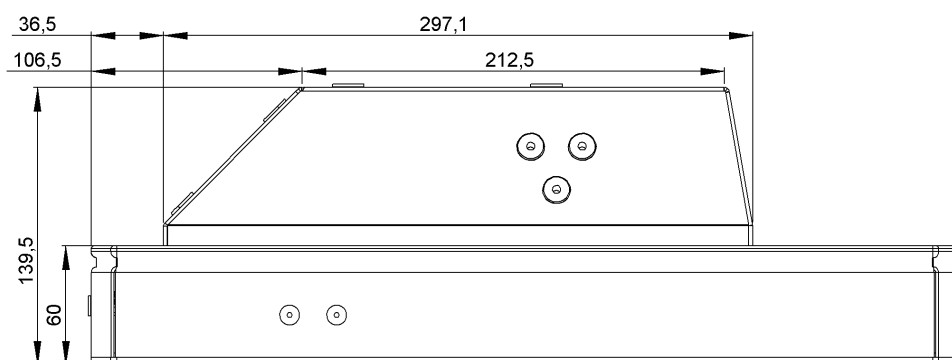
Seitenansicht S19 (alle Maße in mm)
